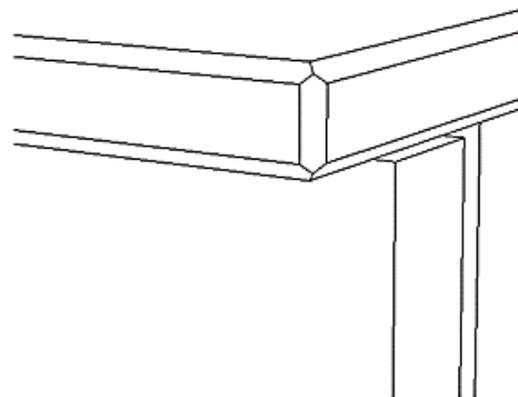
Крепление столешницы из компакт-ламината на корпус кухни.
